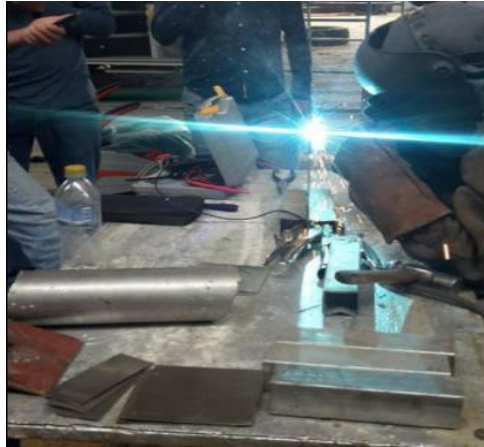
Soldadura en carrocería de buses interprovinciales
